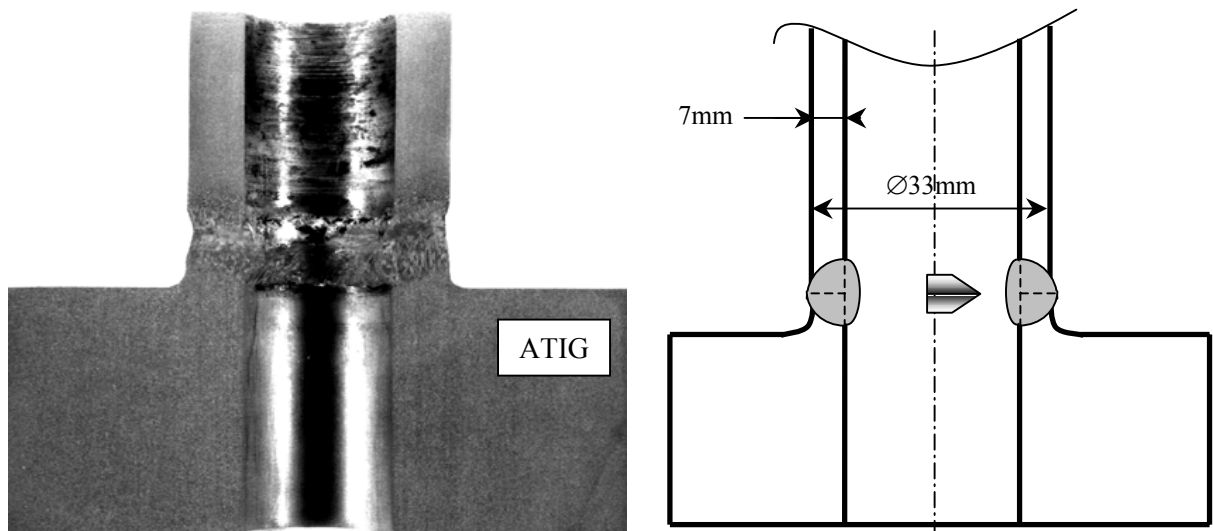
Soudage ATIG tube sur plaque en intérieur tube - courant pulsé 150/130A
